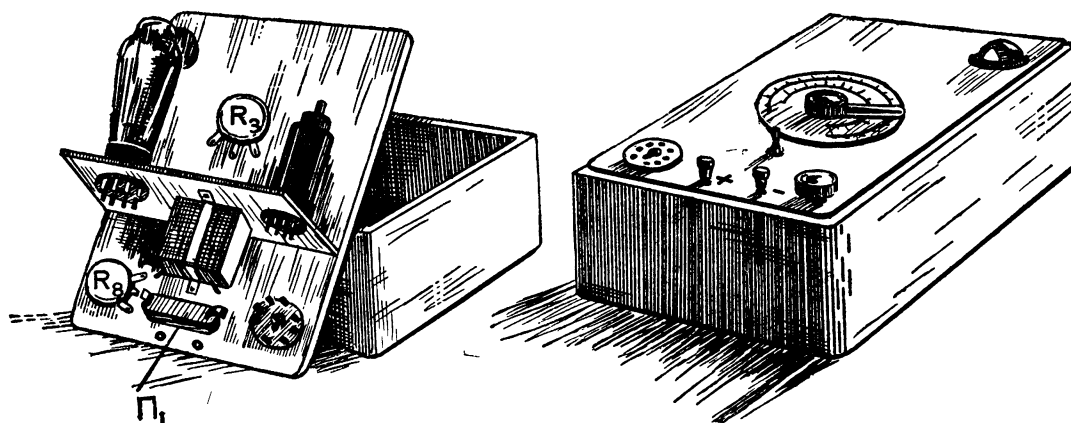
Размещение деталей лампового вольтметра и общий вид прибора.
